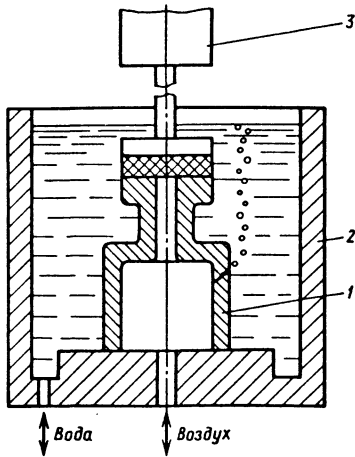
Схема пневматического контроля герметичности отливок (метод "аквариума"): 1 - отливка; 2 - корпус водяной ванны; 3 - прижимное устройство
